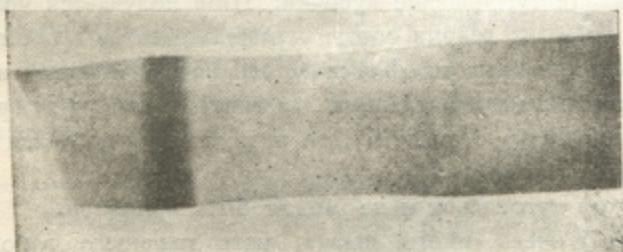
Хорошая сварка. Хороший флюс № 6.
